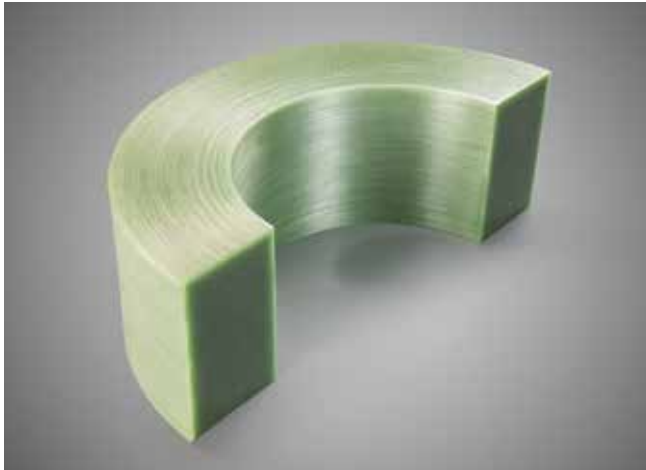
Segment eines 12 cm dicken GFK-Wurzelrings für Rotorblätter
